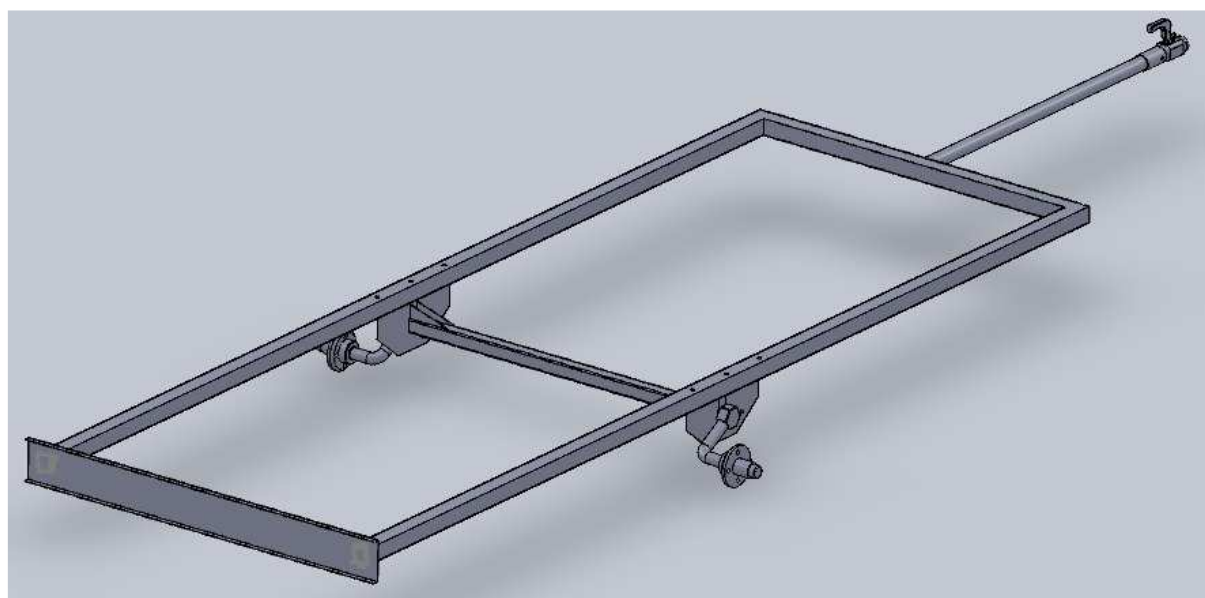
Konstrukční návrh přívesu – varianta 2. Detailní pohled na patku nápravy a čtvercový profil. Zřetelně jsou vidět otvory pro šrouby. Otvory jsou průchozí celým profilem.
